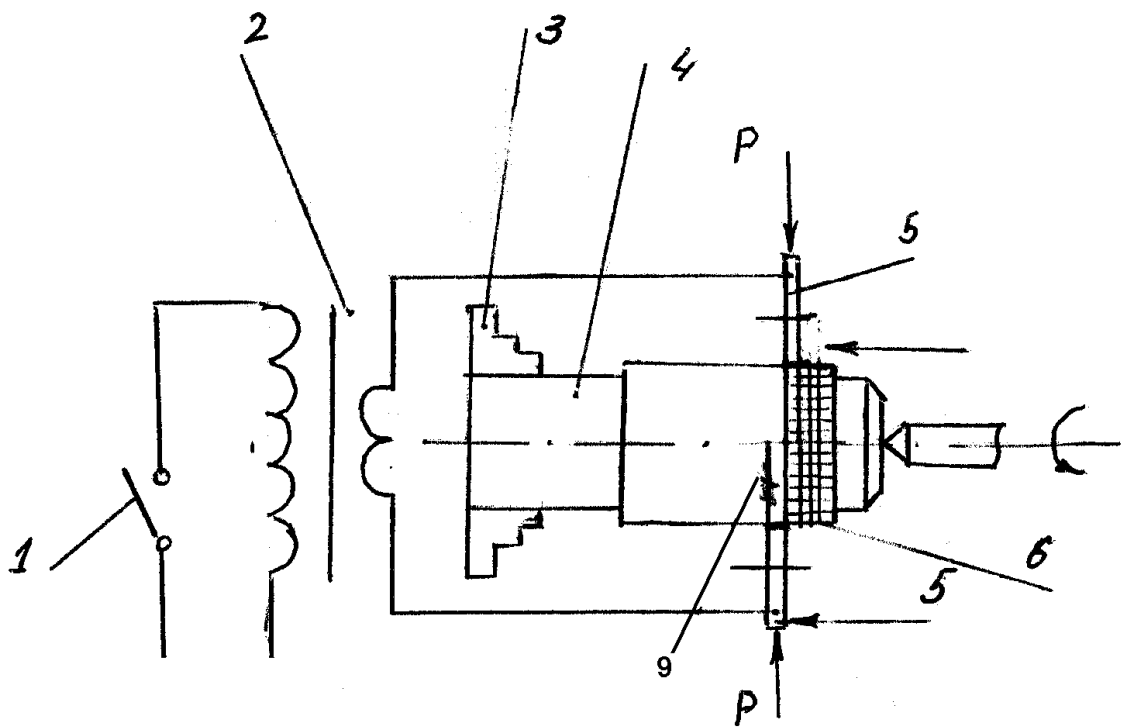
Схема контактной приварки ленты; 1-прерыватель тока; 2-трансформатор; 3-кулачки патрона; 4-восстанавливаемая деталь; 5-сварочные электроды; 6-привариваемая лента
